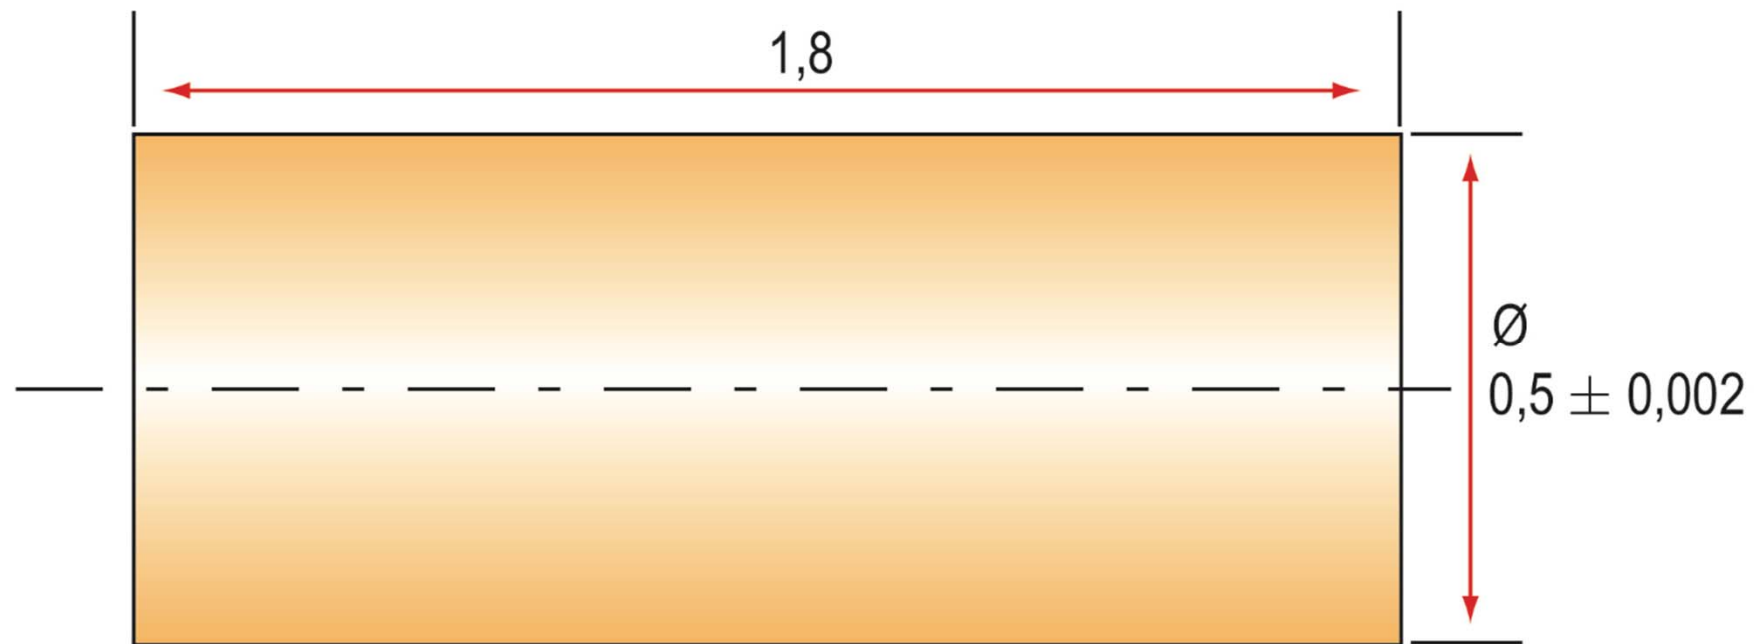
Tolerancia dimensional de un perno.
